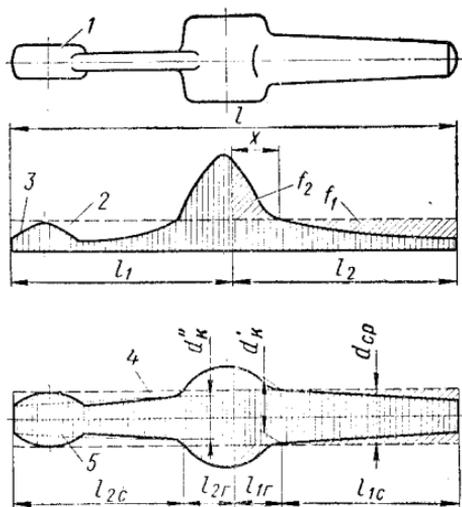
Приведение заготовки с одной головкой и двусторонним стержнем к двум элементарным заготовкам:
